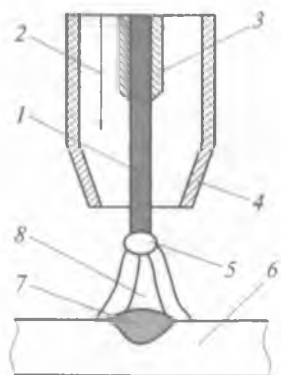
Схема процесса полуавтоматической сварки в среде защитного газа:
